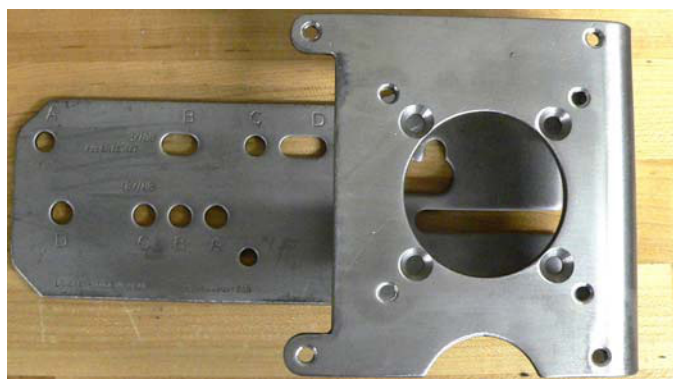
Supporto di montaggio per valvola a movimento alternato per leva standard
